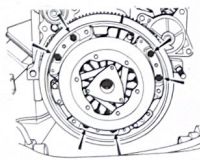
Embrague de un motor tipo 813 (las flechas indican los tornillos que hay que retirar para extraer el mecanismo de presión).
